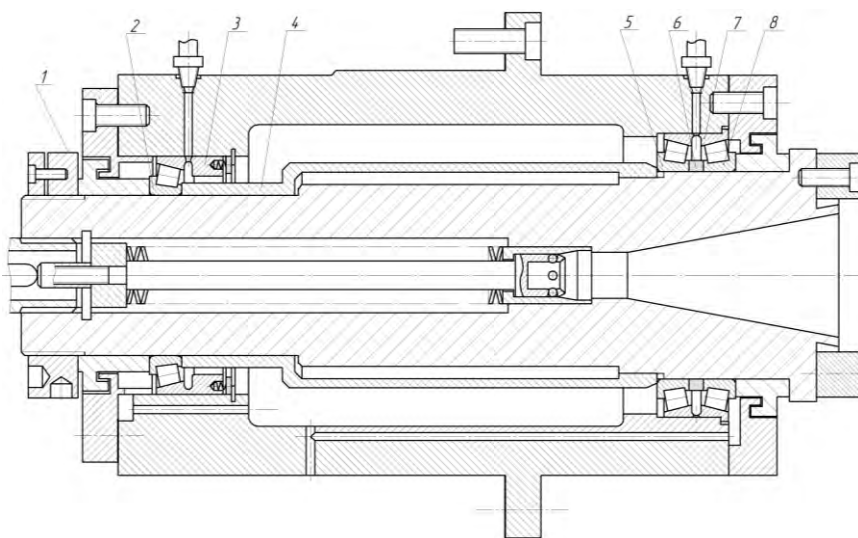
Автономный шпиндельный узел с роликовыми радиально-упорными коническими подшипниками: двухрядным в передней и однорядным – в задней
